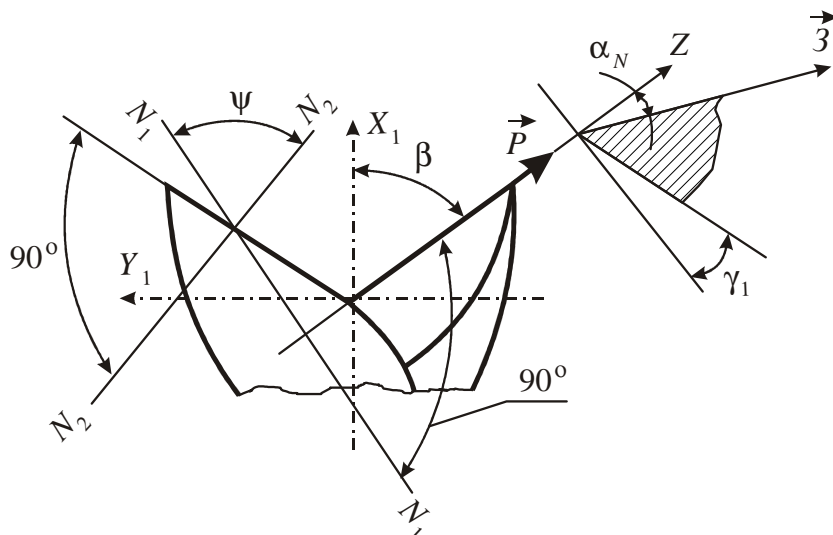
Геометрические параметры сверла с обратным углом при вершине с прямолинейными режущими кромками (ПРК)
